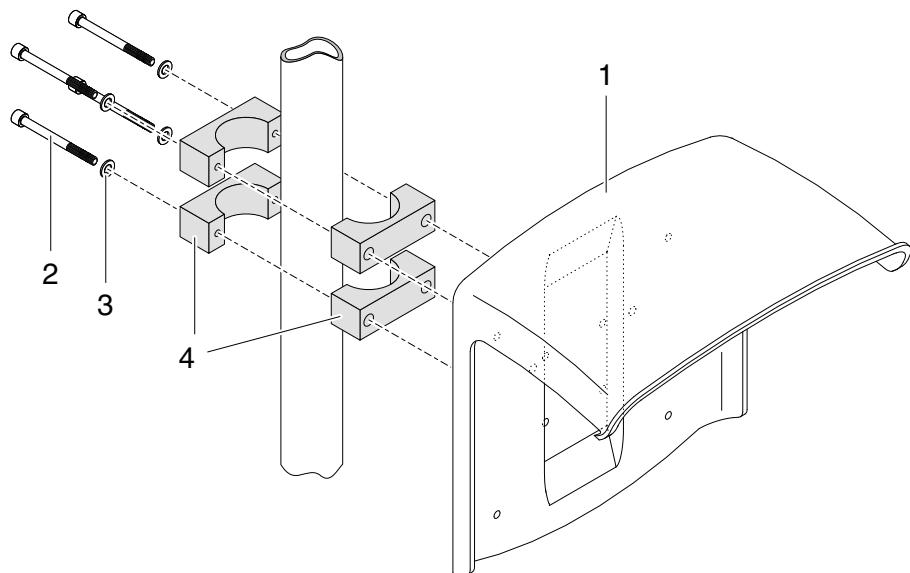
Montagem da blindagem solar SSH/IQ num suporte de montagem
